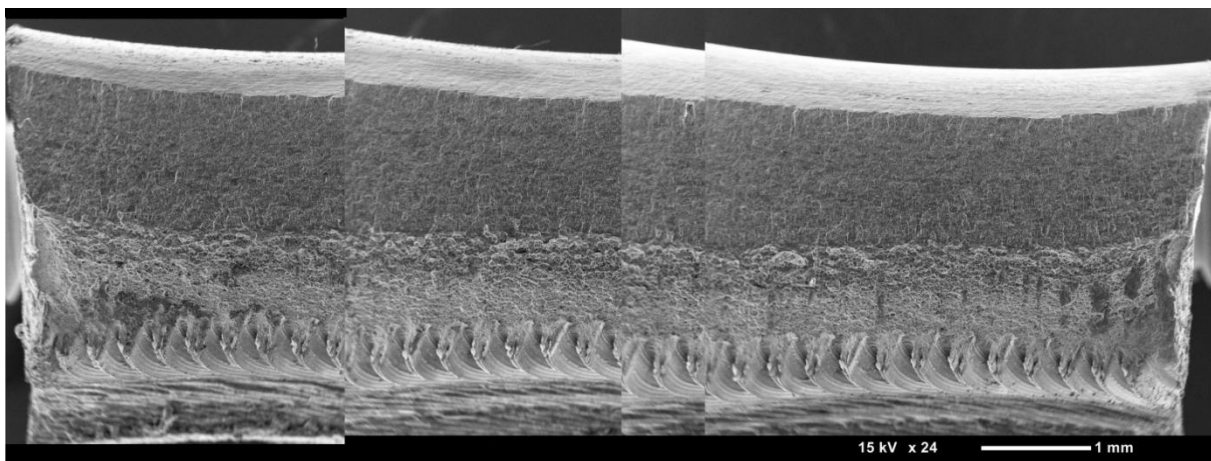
Übersichtsaufnahme der Bruchoberfläche einer Schweißung des Parametersatzes IMWF-11-00002 ($n=1000 \text{ min}^{-1}$, $v_x=250 \text{ mm/min}$)
